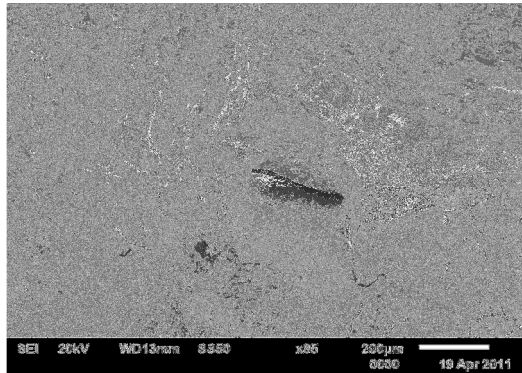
Falta de fusión en la soldadura.
